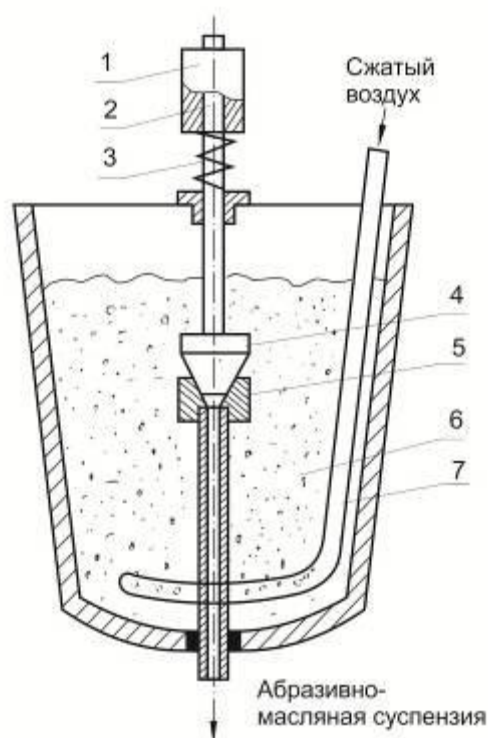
Схема бункера-дозатора: 1 - электромагнит; 2 - якорь; 3 - пружина; 4 - клапан; 5 - насадка; 6 - абразивно-масляная суспензия; 7 - трубка спираль.
